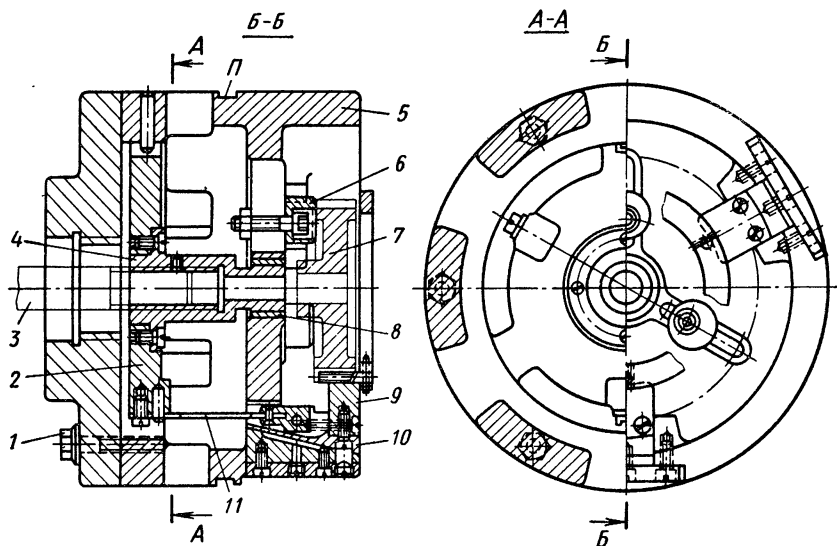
Патрон для крепления зубчатых колес при шлифовании отверстий
